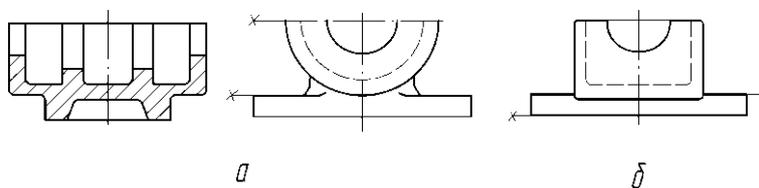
Корпус подшипника: а - нетехнологичная; б - технологичная конструкция
